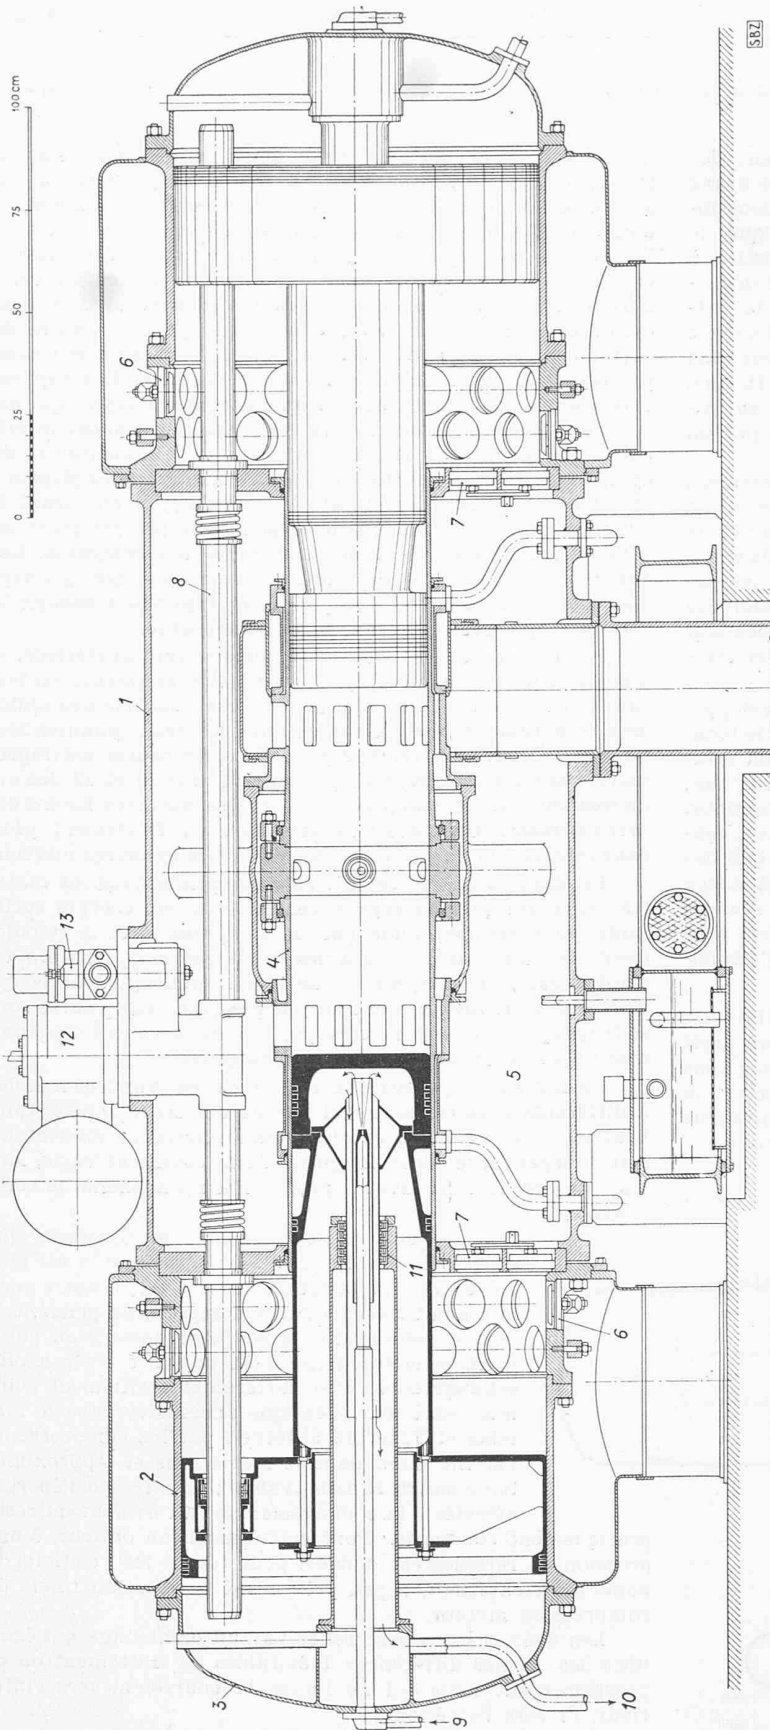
Coupe longitudinale par le plan vertical d'un générateur à pistons libres GS-34
